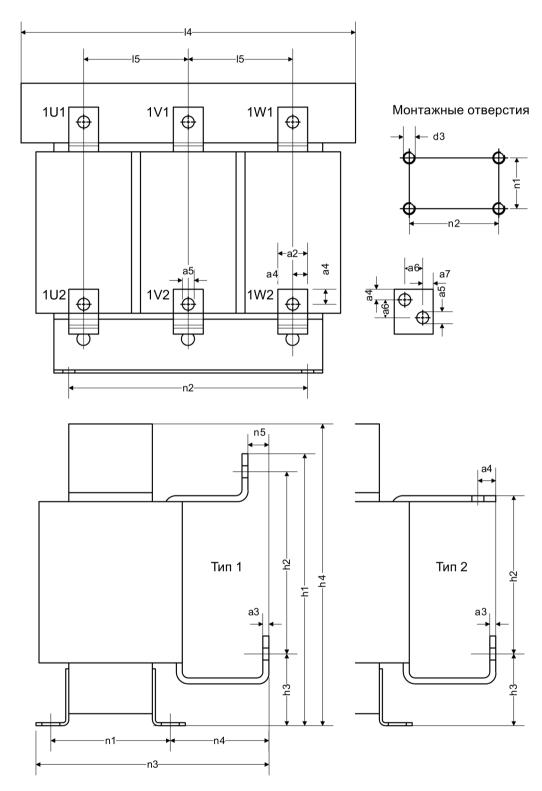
Габаритный чертеж дросселя двигателя
